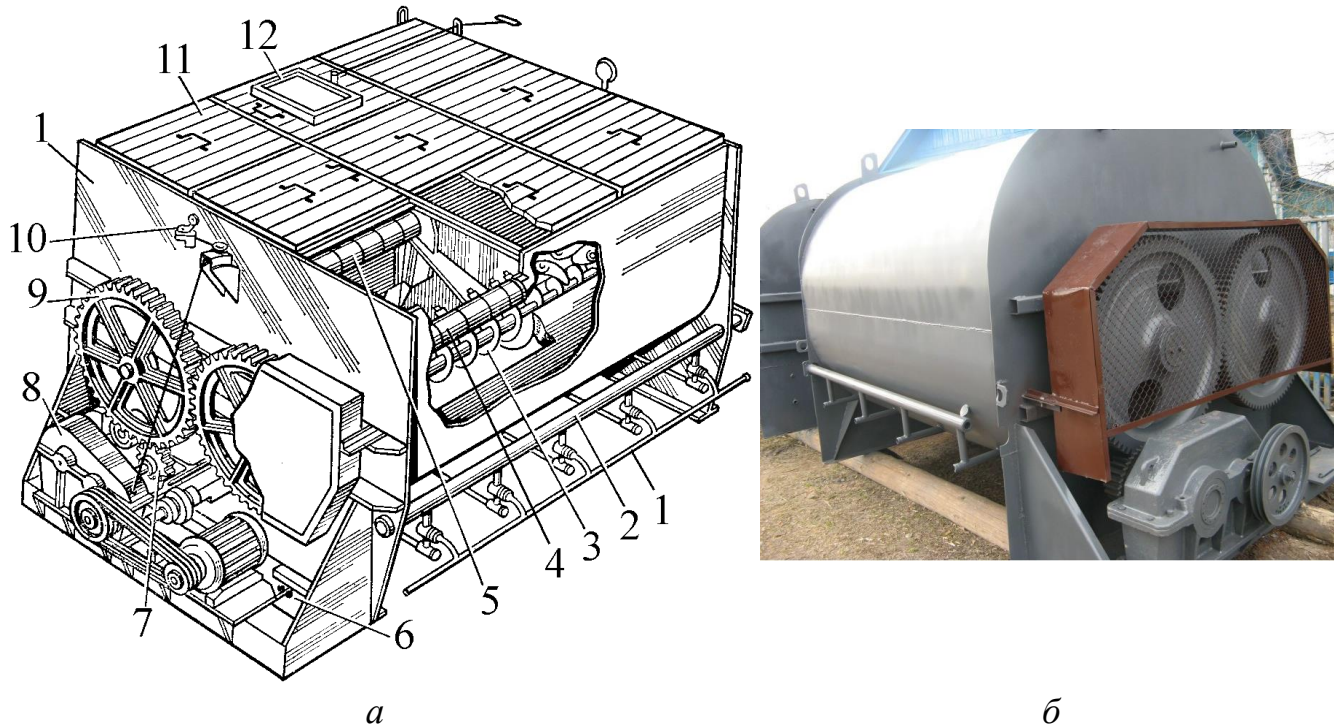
Змішувач компонентів раціону С-12: *а* – схема структурна; *б* – загальний вигляд; 1 – корпус; 2 – розподільник пари; 3 – шнек вивантажувальний; 4, 5 – лопатеві мішалки; 6 – електродвигун; 7 – ведуча шестерня; 8 – редуктор; 9 – шестерня ведена; 10 – кронштейн; 11 – знімні кришки; 12 – люк завантажувальний [5, 12]
